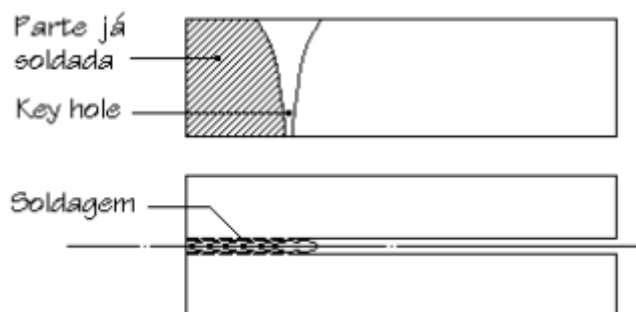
Soldagem penetrante - Técnica do "key-hole"
